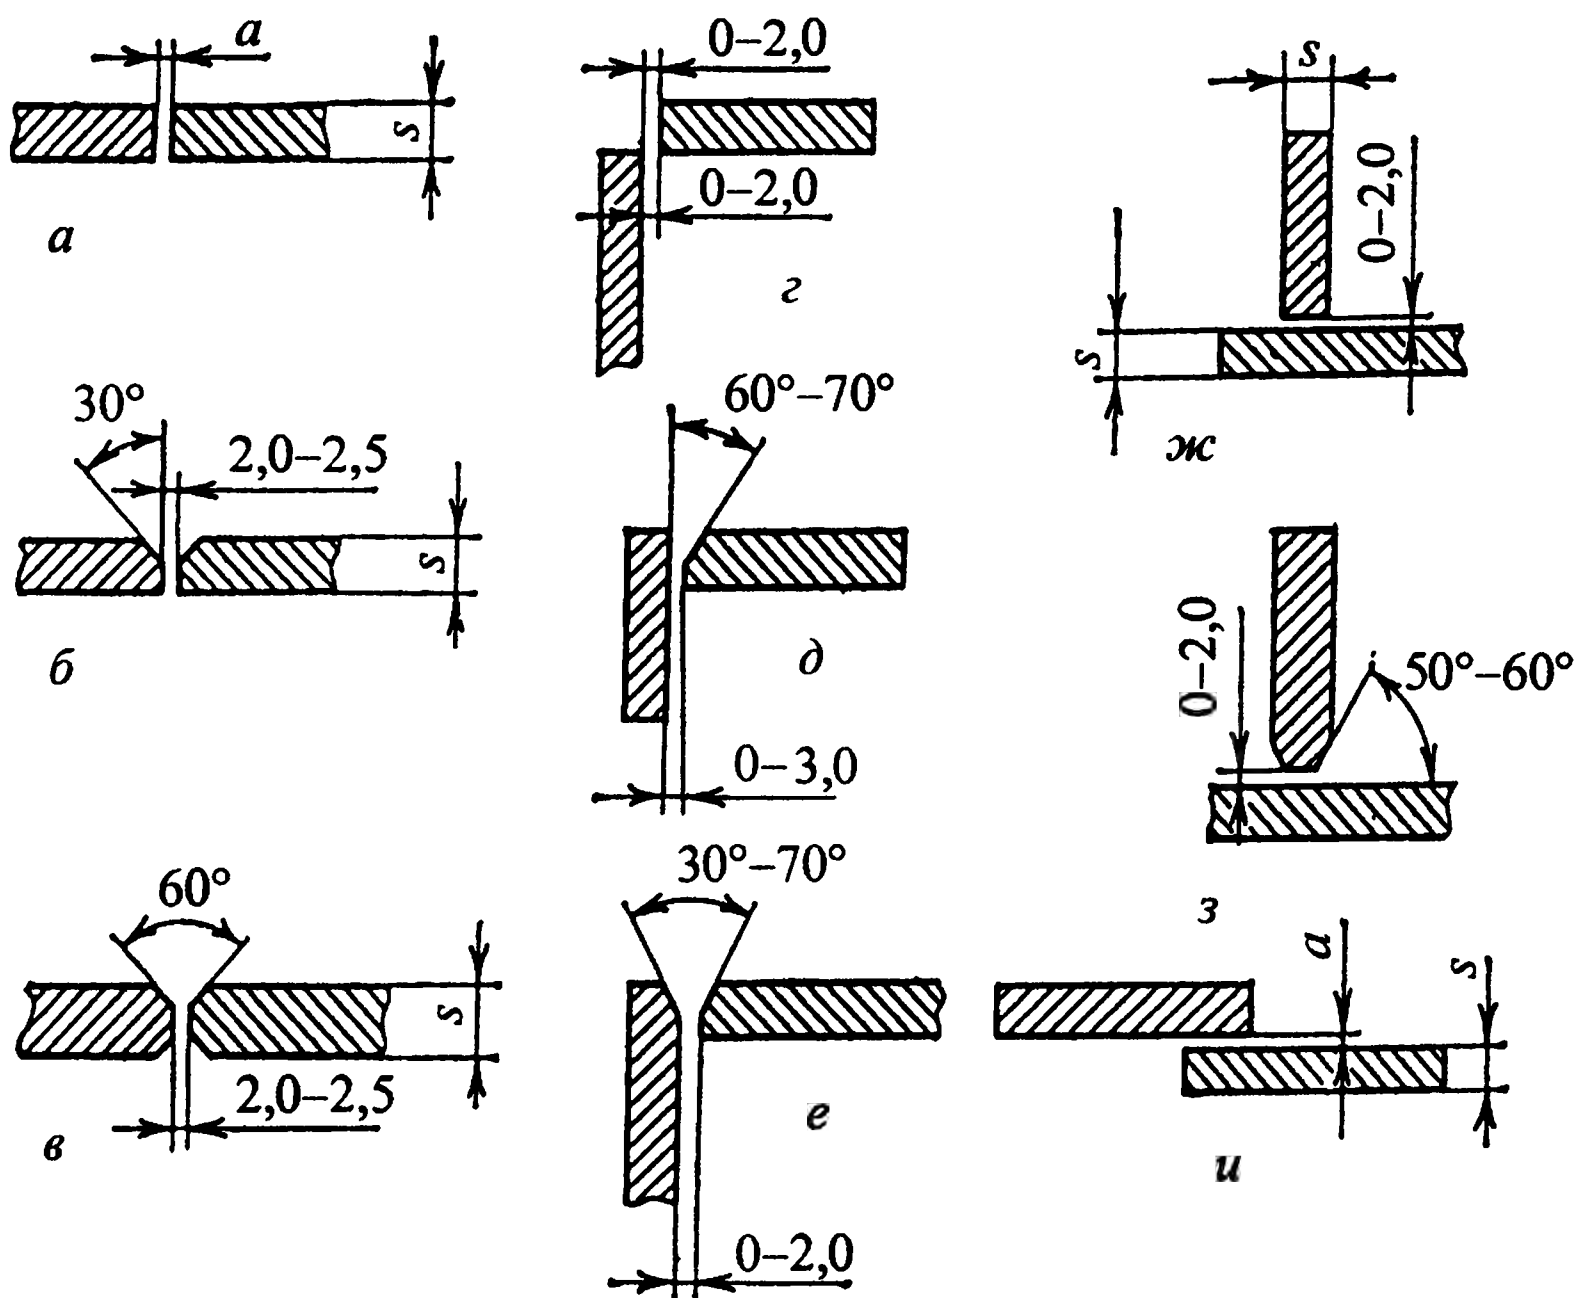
Рекомендуемые типы соединений для ручной дуговой сварки
